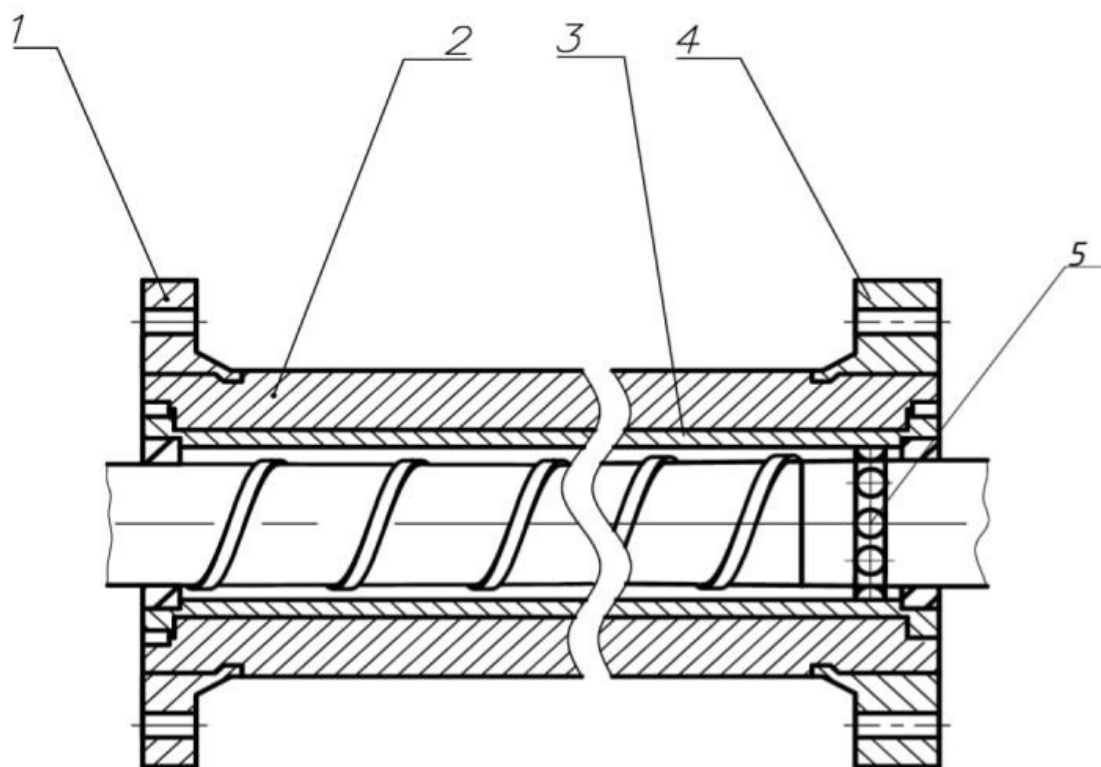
Вигляд модернізованої конструкції корпусу [5]: 1 – фланець правий; 2 – корпус; 3 – гільза; 4 – фланець лівий; 5 – тіла обертання
